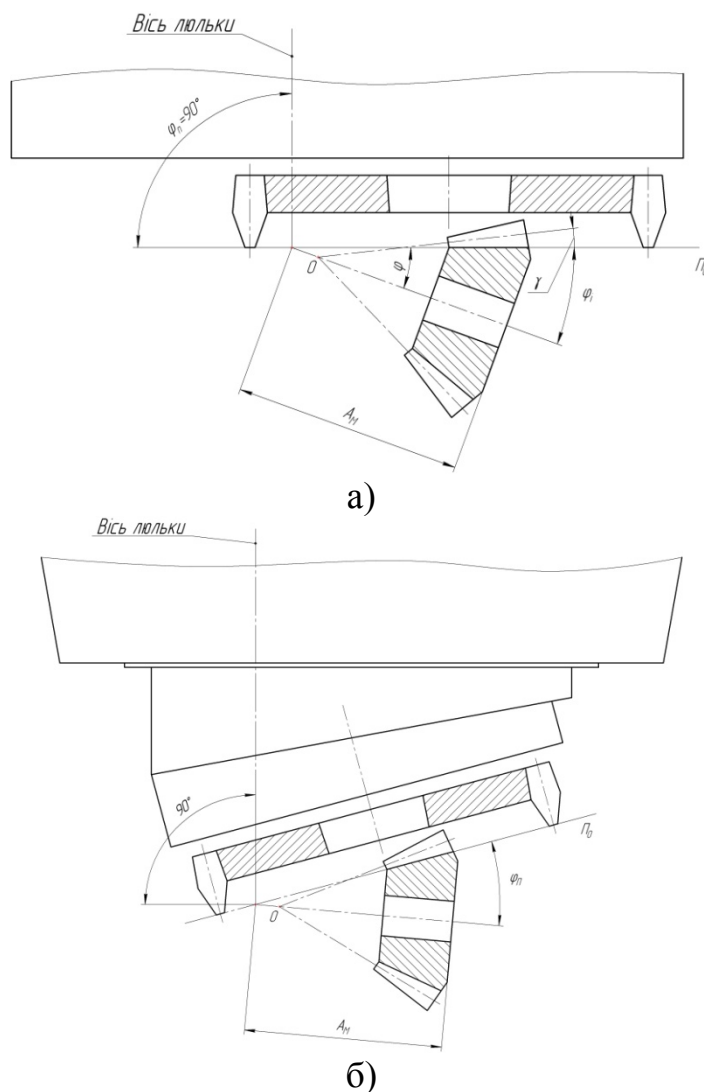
Производящее колесо станка: а) плосковершинное; б) конусовершинное
